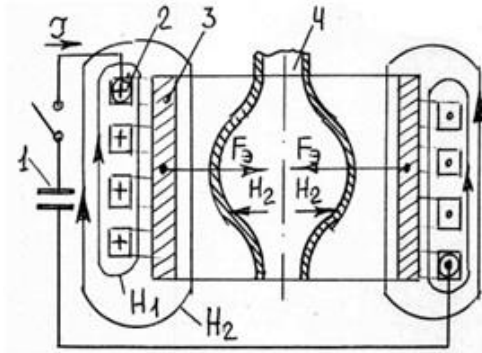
Схема індукційного формоутворення: 1 – батарея конденсаторів; 2 – збудник; 3 – заготовка; 4 – матриця
